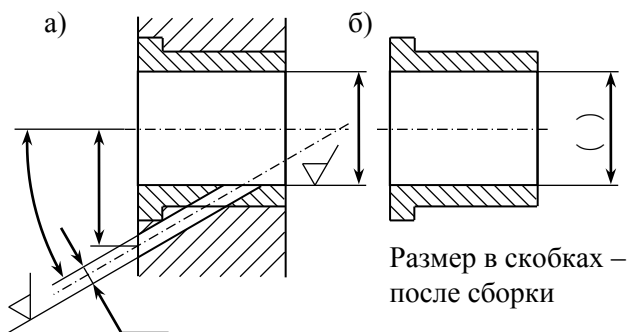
Размеры, предельные отклонения и шероховатость поверхностей элементов изделия
